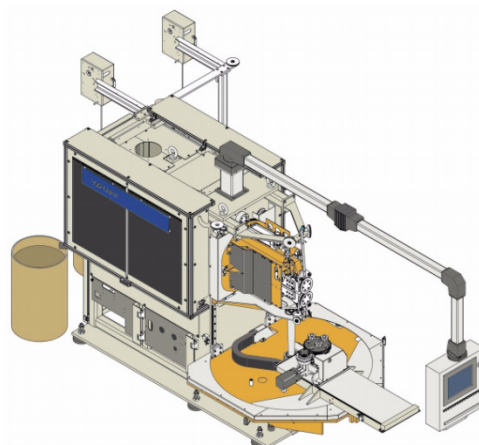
Figura esquemática do equipamento utilizado na soldagem por costura desse trabalho
